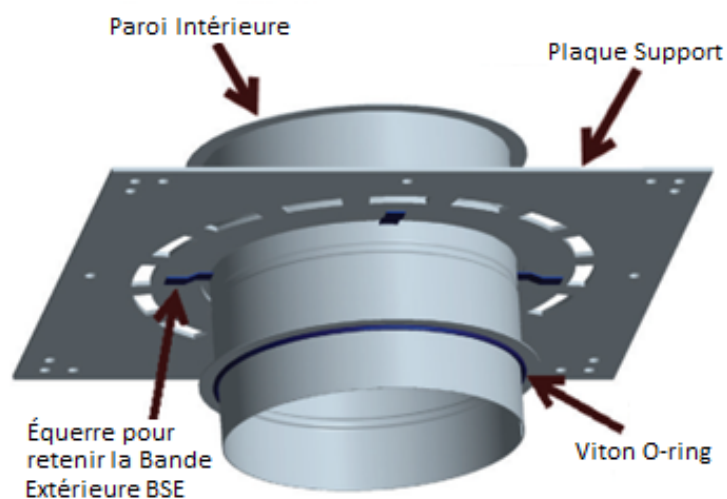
Plaque d'Ancre Ventilée avec Longueur (APVL)
